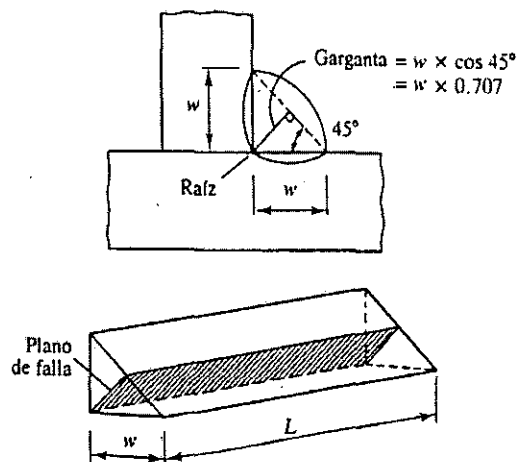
Geometría de un Cordón de Soldadura Tipo Filete
